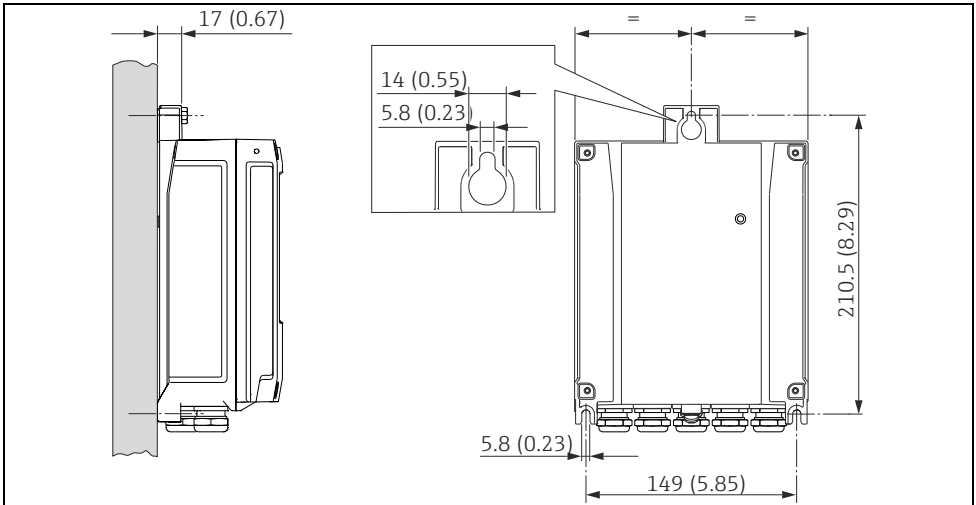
1. Bohrlöcher bohren. 2. Dübel in Bohrlöcher einsetzen. 3. Befestigungsschrauben leicht einschrauben.
